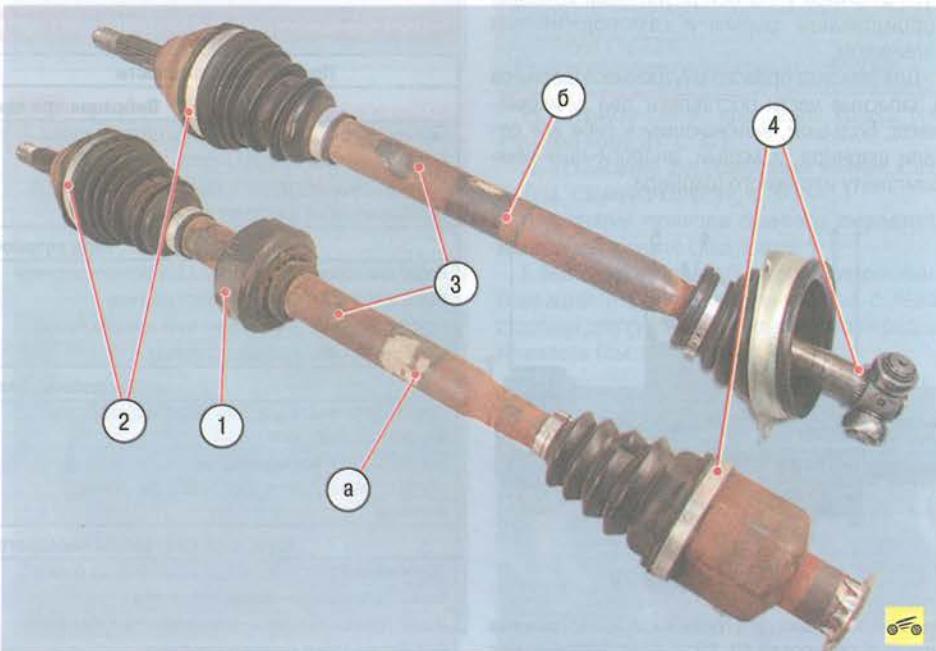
Приводы передних колес: а – привод правого переднего колеса; б – привод левого переднего колеса; 1 – динамический демпфер; 2 – наружные шарниры; 3 – валы приводов передних колес; 4 – внутренние шарниры
